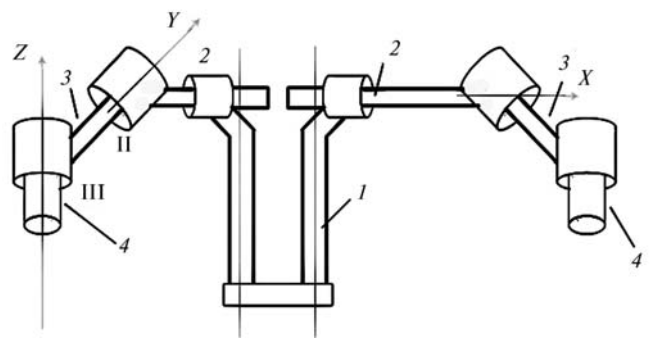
Схема корпуса ДШР с руками: 1 — корпус; 2 — ключица; 3 — плечо; 4 — предплечье
